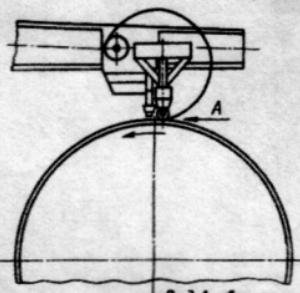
Пристосление для притягивания кронок и подкладочному кольцу перед сваркой головкой
